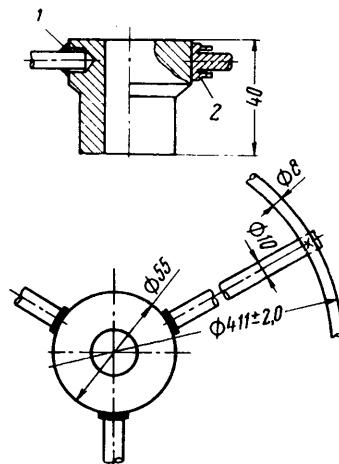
Соединение спицы со ступицей каркаса рулевого колеса, выполненное с применением дуговой сварки и сварки трением:
